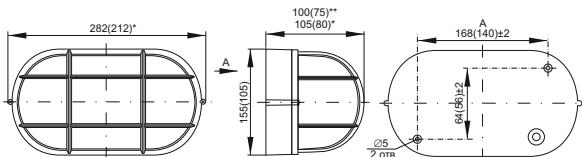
Габаритные и установочные размеры светильника НПП 1202
